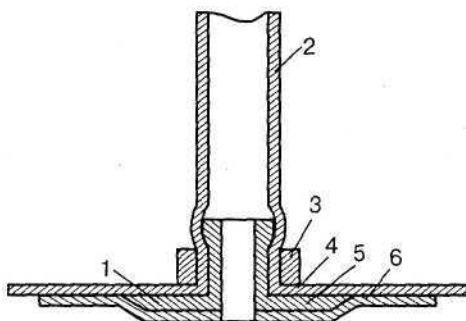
Вклейка штуцера: 1 — штуцер; 2 — резиновая трубка; 3 — резиновое кольцо; 4 — накладка из тонкого прорезиненного материала; 5 — баллон; 6 — кольцо из прорезиненного материала
